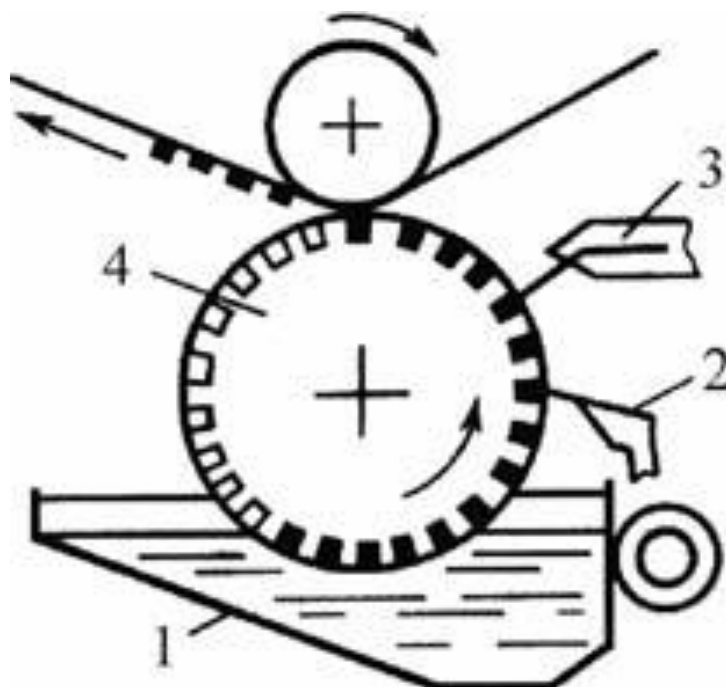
Схема установки ракеля: 1 - ящик, що відкидається, з фарбою; 2 – попередній (опорний) ракель; 3 – головний (крутий) ракель; 4 – формний циліндр.
